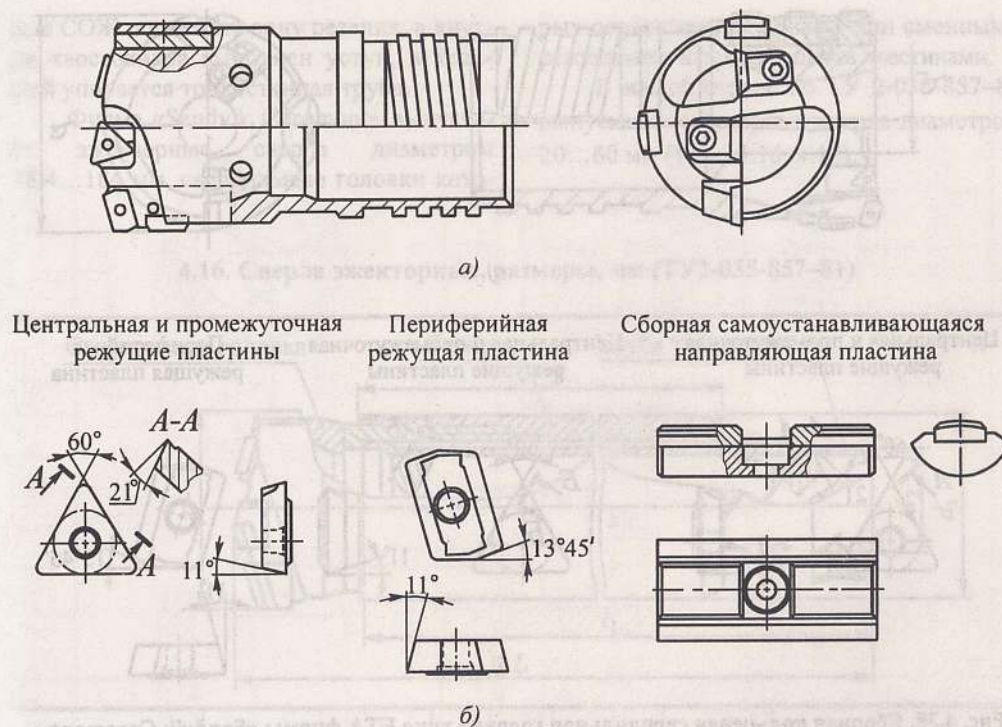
Сборная сверлильная головка типа БТА T-MAX фирмы «Sandvik Coromant»: а – общий вид головки; б – твердосплавные сменные режущие и сборные самоустанавливающиеся направляющие пластины
